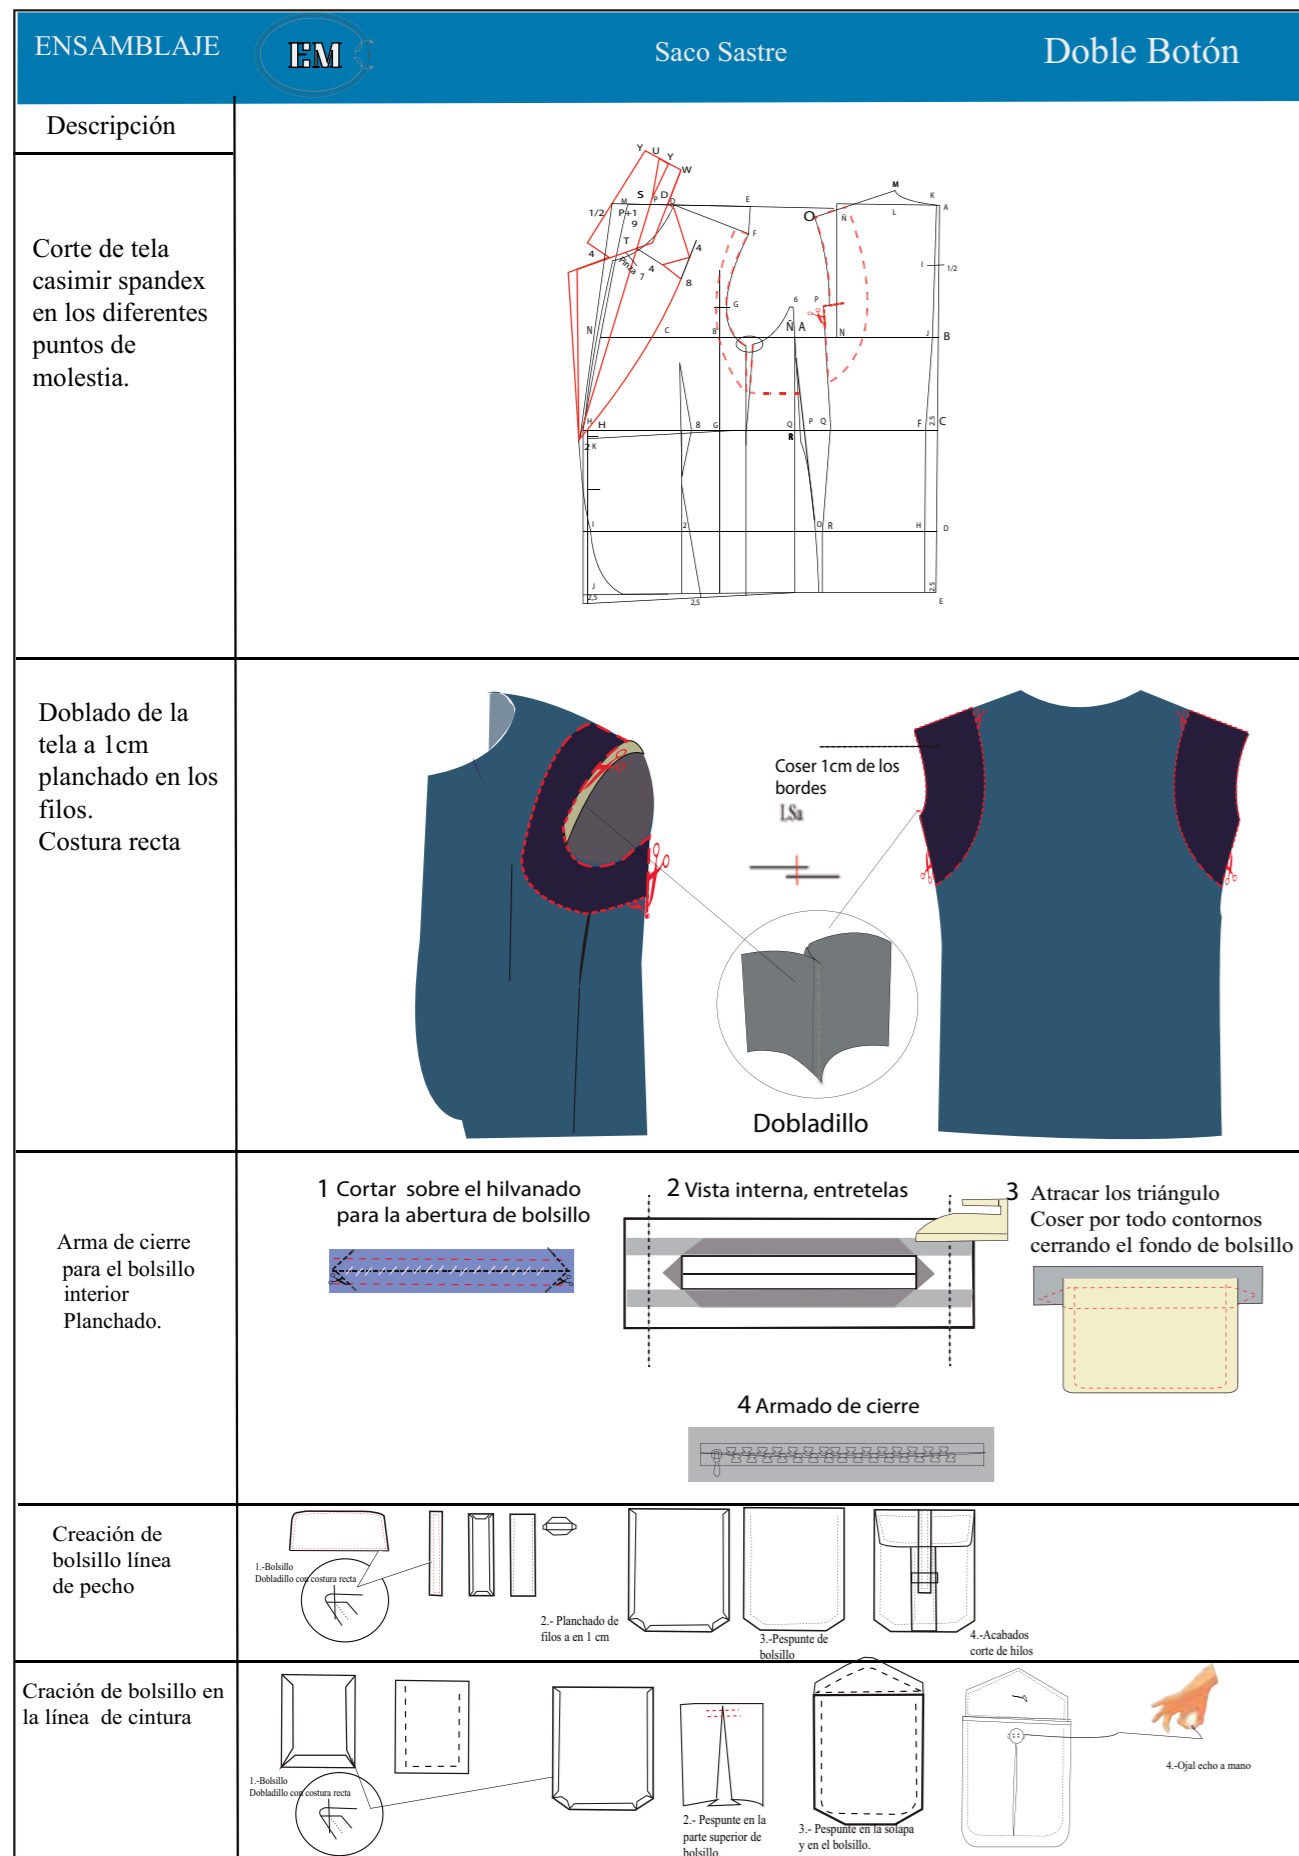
Ensamblaje saco sastre doble botón Fuente: Elaboración propia
